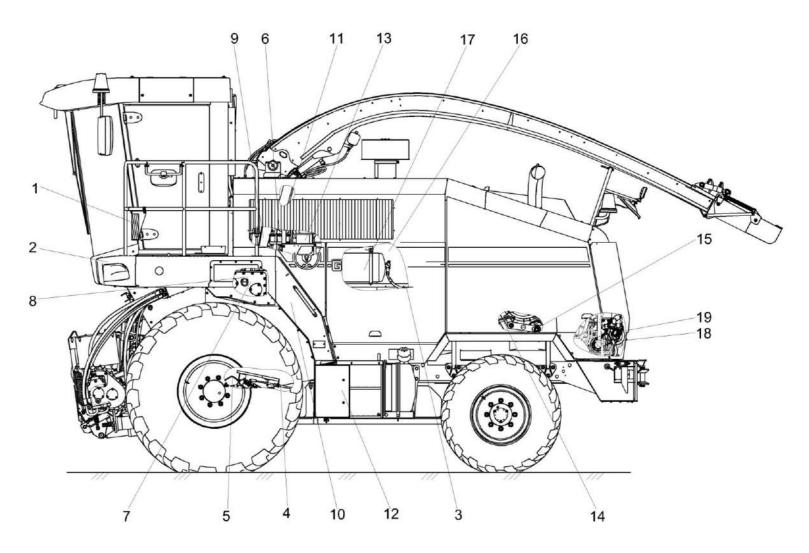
Комбайн кормоуборочный самоходный КВС-80-7-0100000-01 (вид слева)
